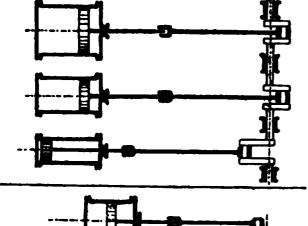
Dreifach - Expansions-maschine. 3 Kurbeln unter 1200 versetzt. Sehrgleichmässiger Gang.
